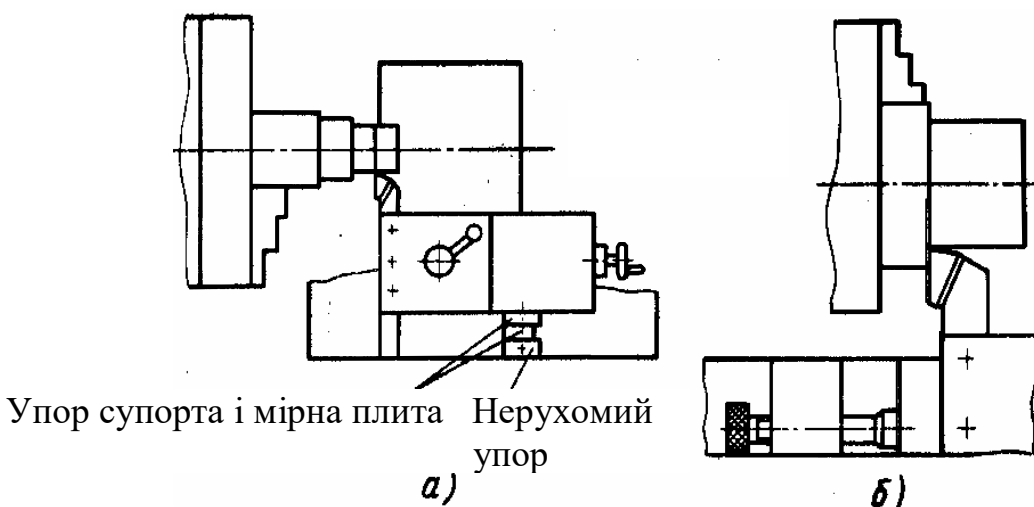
Схеми обробки заготовок з використанням упорів
